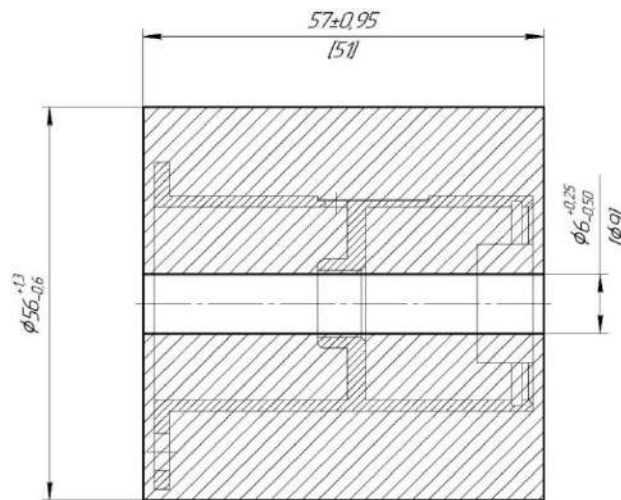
Креслення заготовки отриманої з трубного прокату
